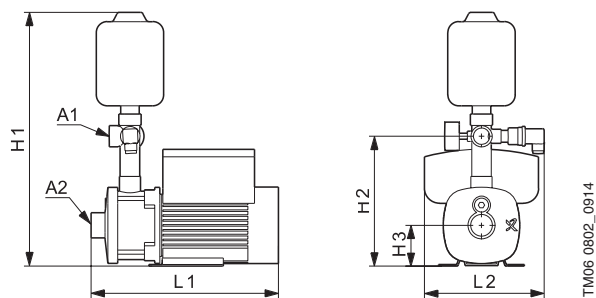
Габаритные и присоединительные размеры насосов СМЕ
